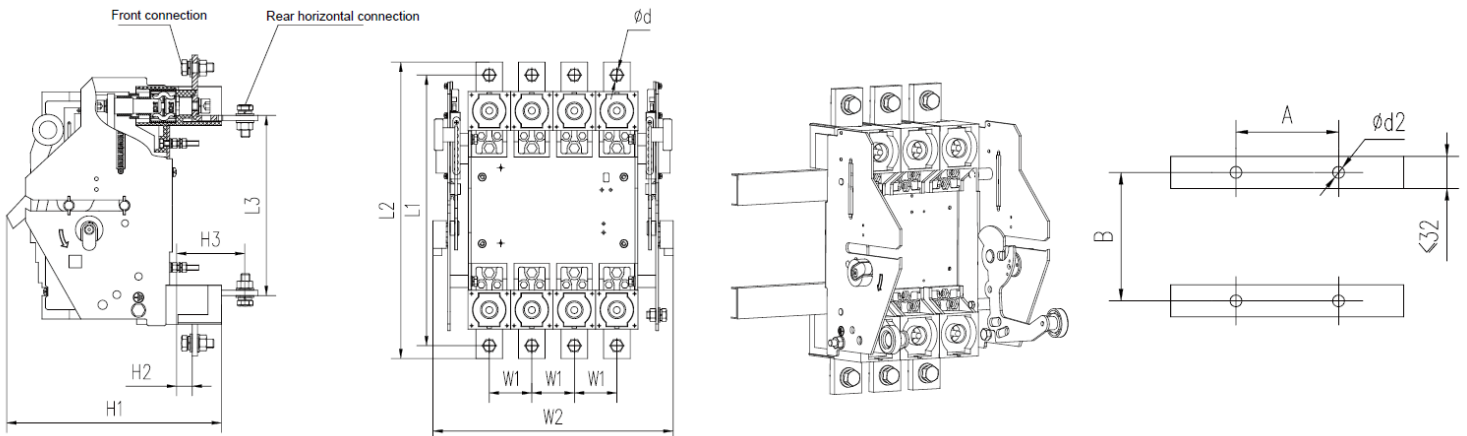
Габаритные размеры выкатного присоединения на выключатели автоматические
